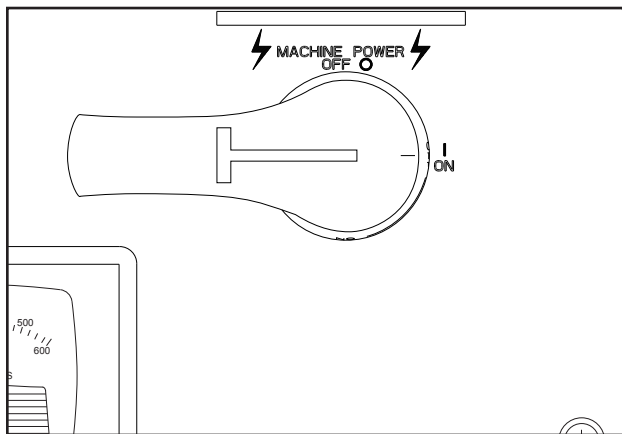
Sezionatore principale nella posizione di attivazione (On)
